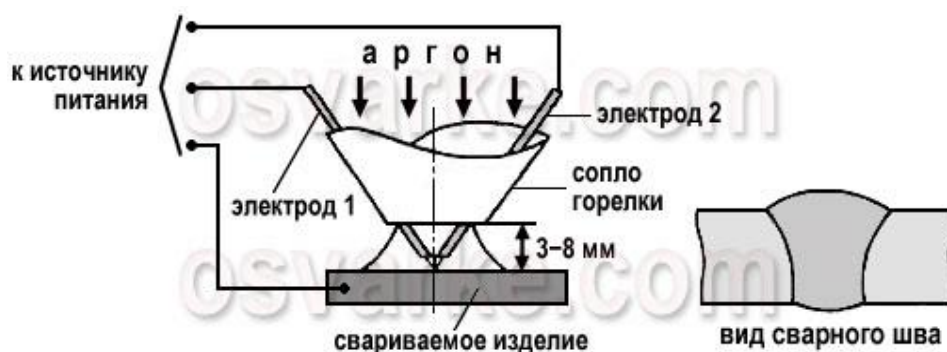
Схема выполнения сварки трёхфазной дугой
